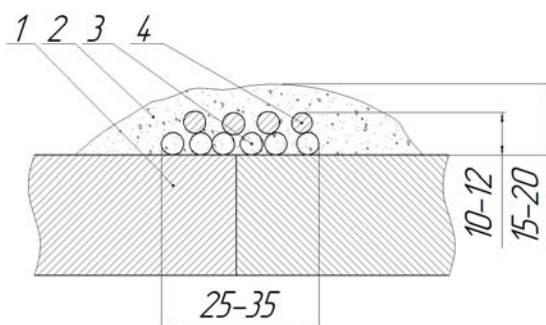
Присадка ППБрХТ 22-2. 1) Основной металл БрХ08; 2) смесь флюсов АН-26 и АФ-4А; 3) Проволока ППБрХТ22-2; 4) Проволока М1
